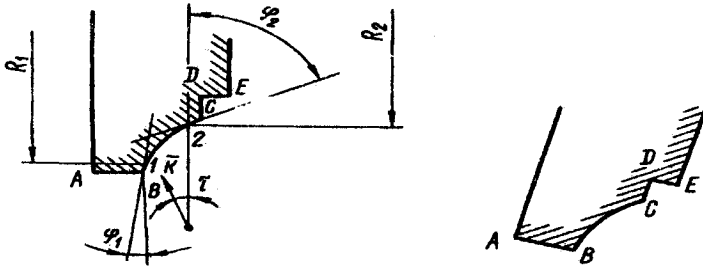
Схема установки деталі при фрезеруванні затиловочною фрезою
